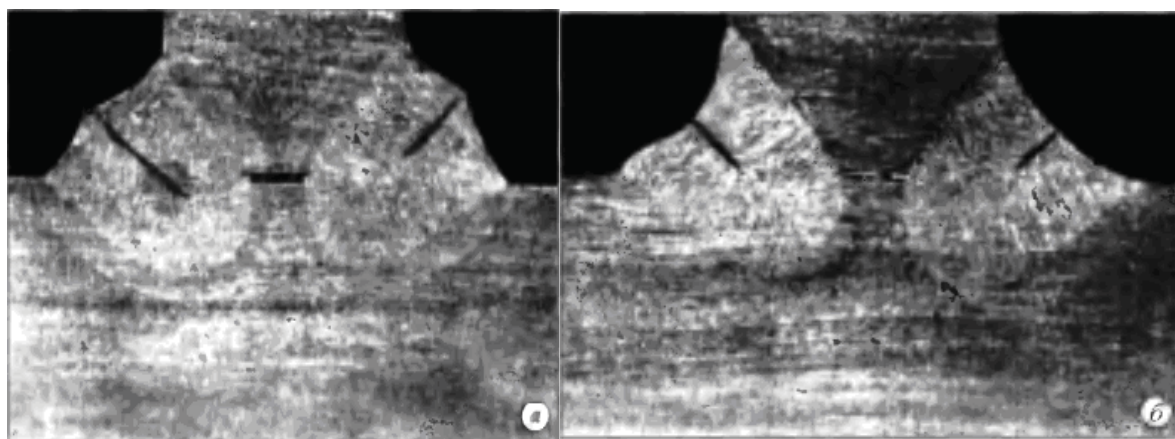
Расположение трещин по сечению шва (дуговая сварка):
